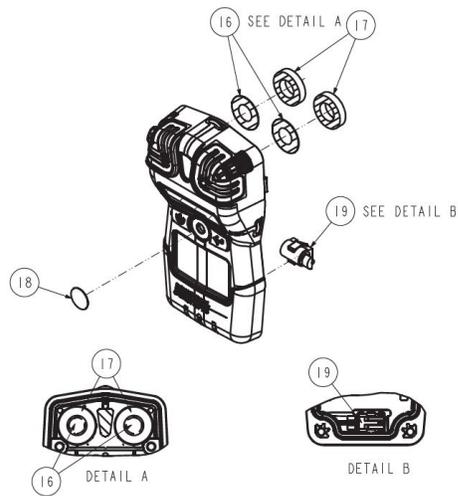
Ensamblaje de la parte superior de la cubierta del Tango TX1 desmontado
